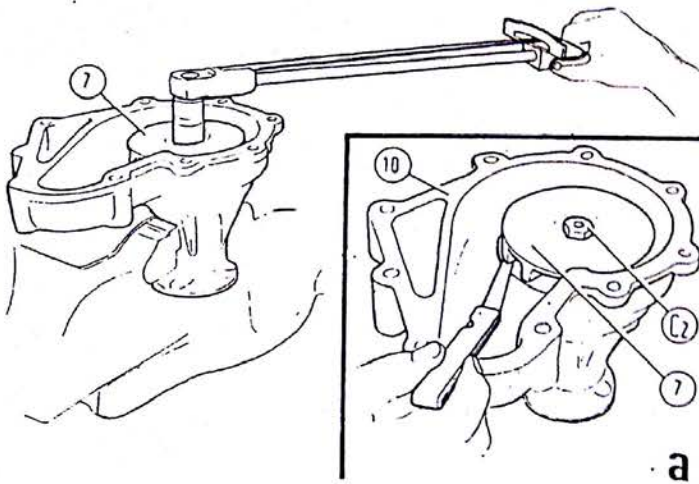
/12 - Serrage de l'écrou (C2) de turbine avec la clé dynamométrique.
